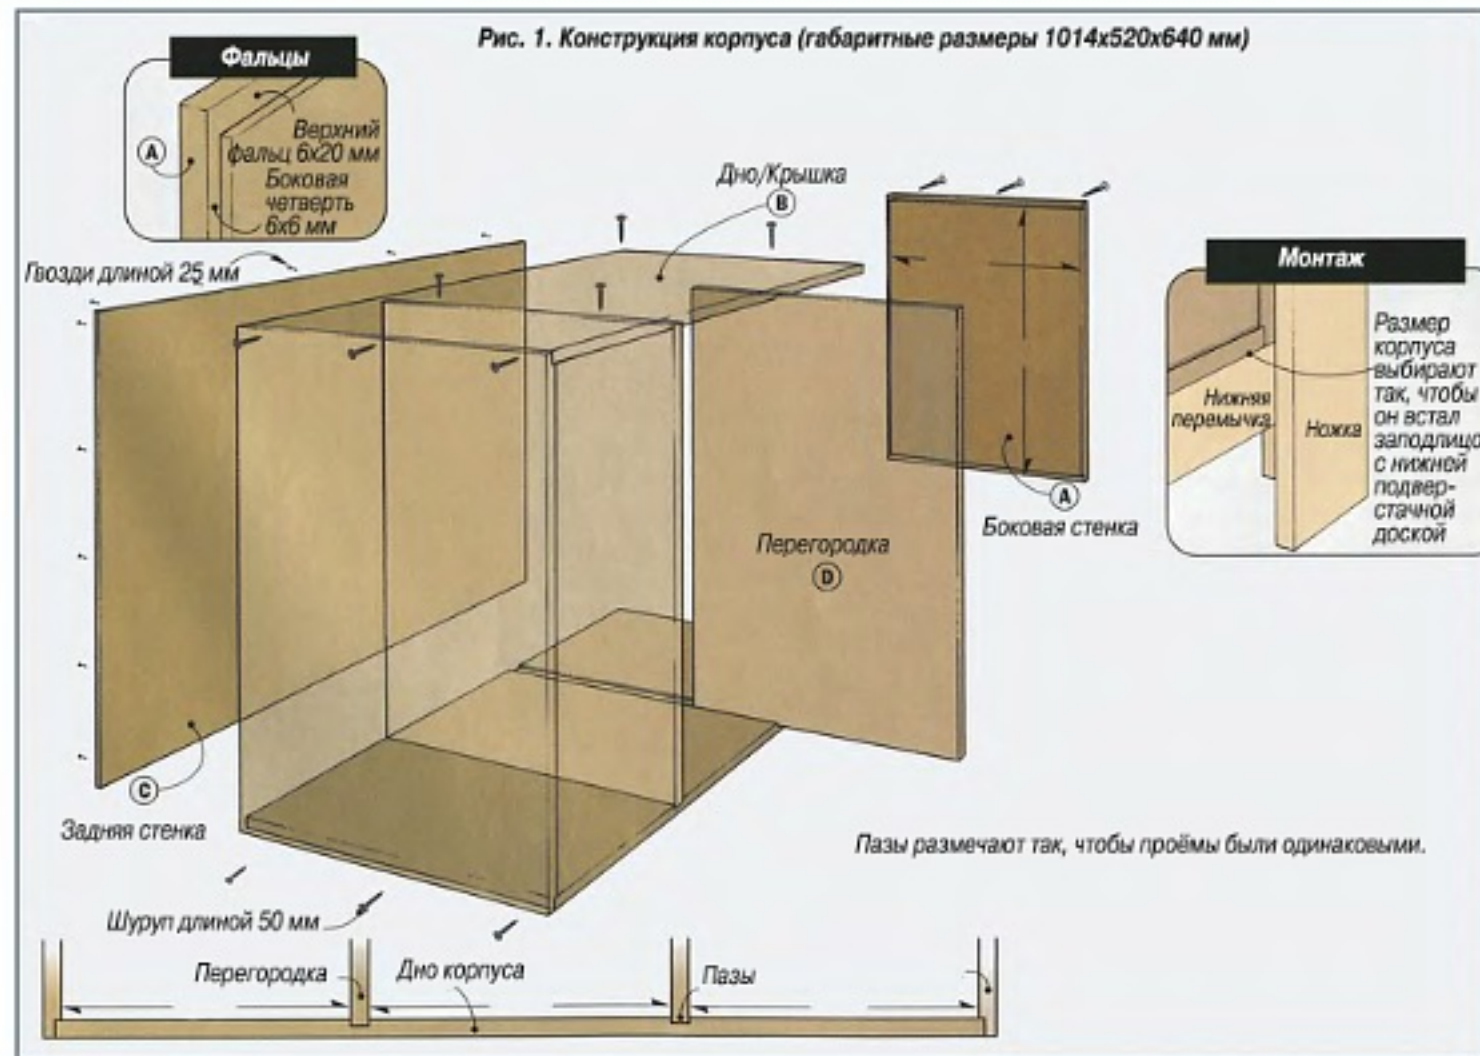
Конструкция корпуса (габаритные размеры 1014x520x640 мм)
